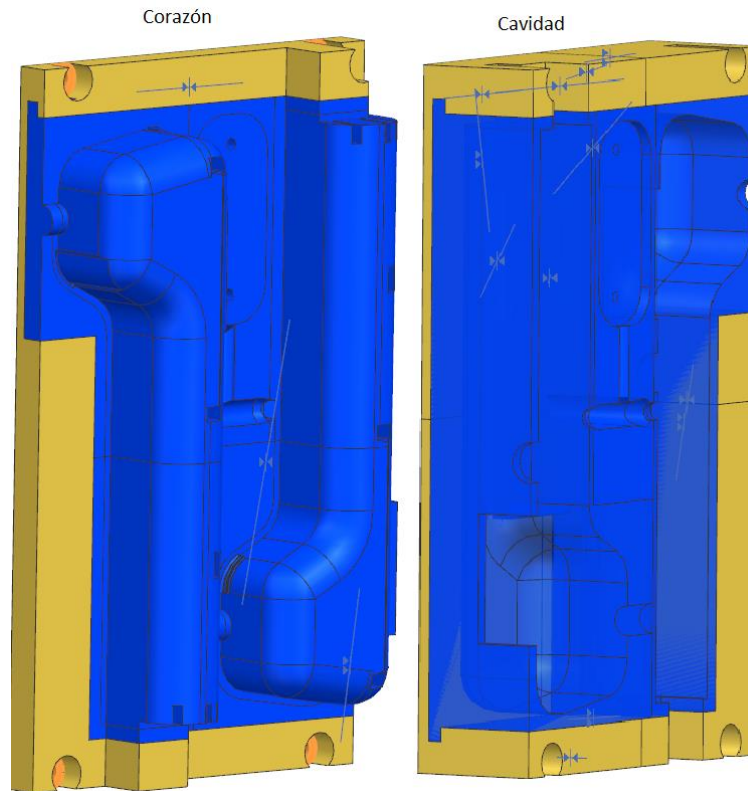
Vista isométrica del prototipo modular de las placas de cavidades y corazones seccionado por material.
